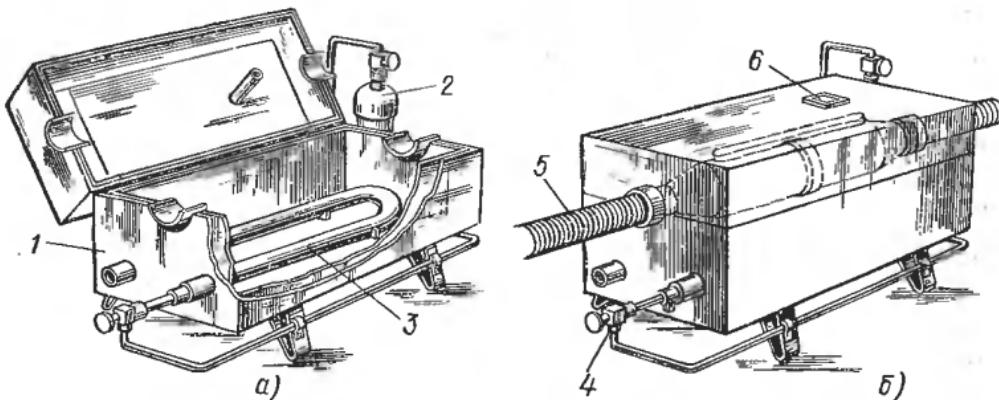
Обогревательная камера для эпоксидных соединительных муфт:
